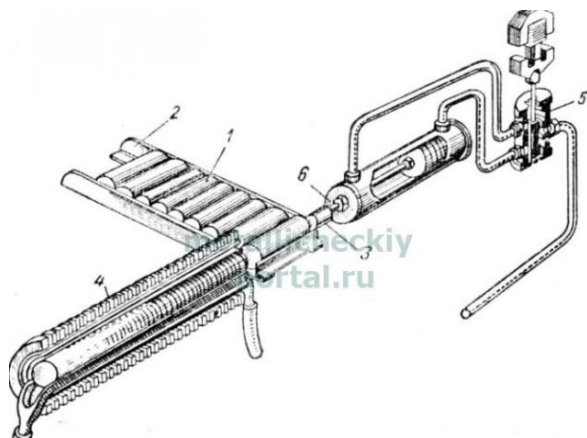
схема работы лоткового загрузочногomeханизма с пневматическим толкателем для загрузки в индукционный нагреватель коротких круглых заготовок
